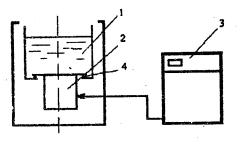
Схема ультразвуковой установки для очистки изделий
